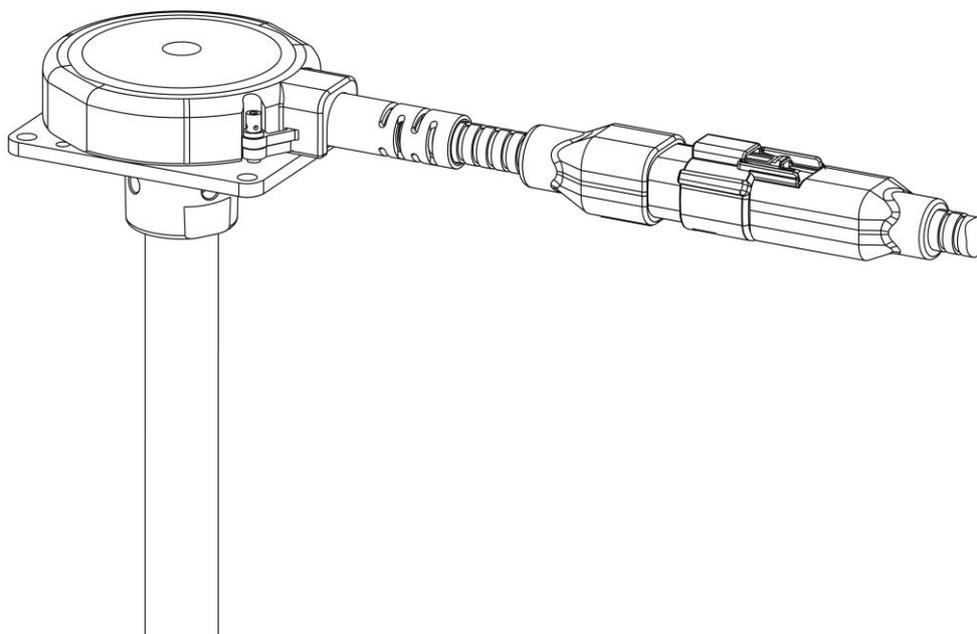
Устройство ДУТ серии Siensor D100 – внешний вид
